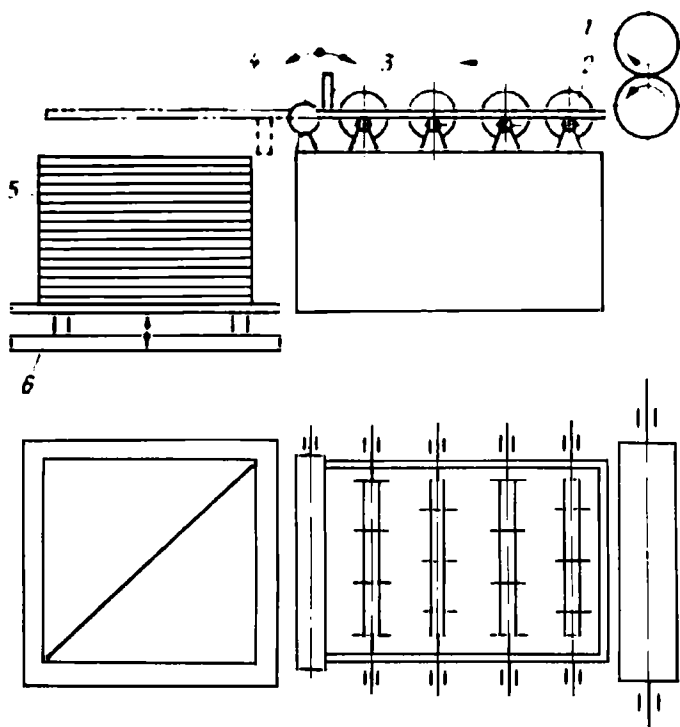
Устройство для механизации сборки пакетов шпона конструкции фирмы «Рауте»
